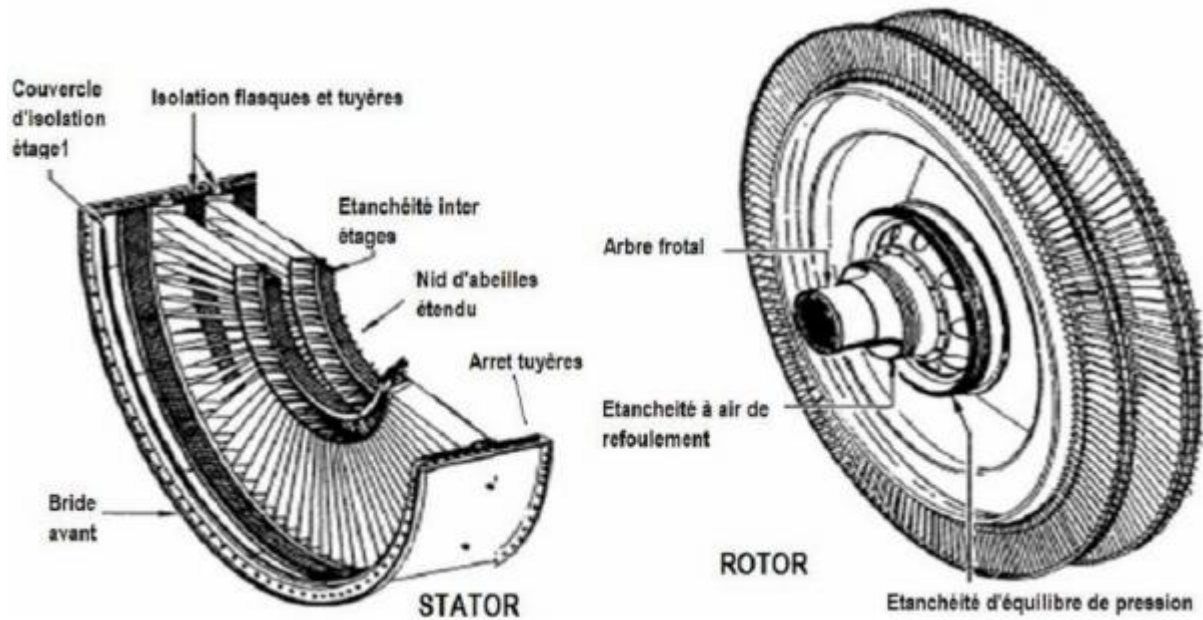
Boîtiers de rotor et stator de la turbine de puissance
